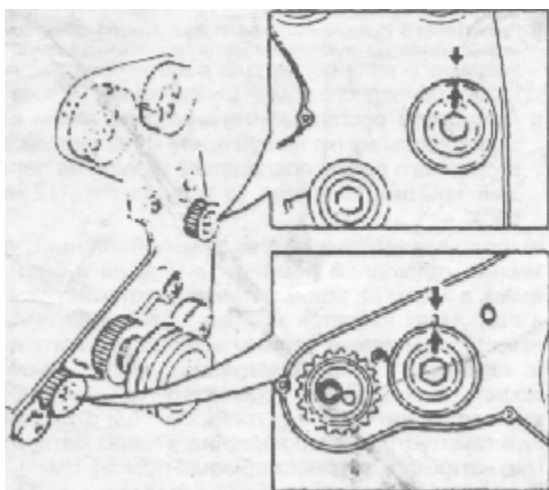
Установка балансировочного вала — Двигатель В234F
